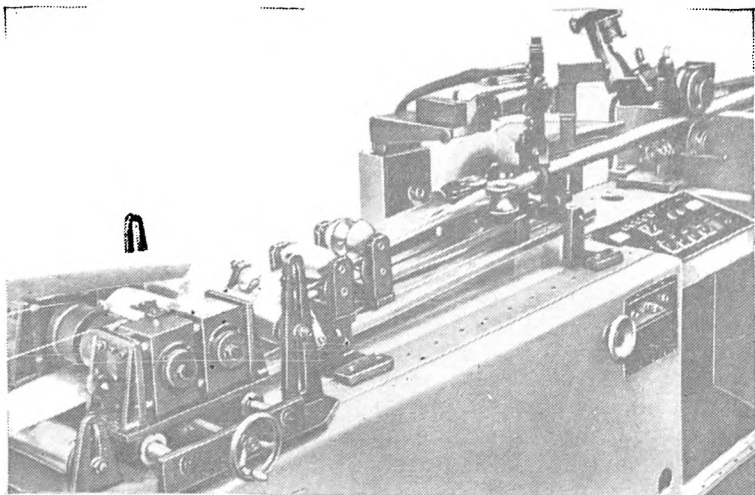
Общий вид формирующего механизма машины «Унивема».
